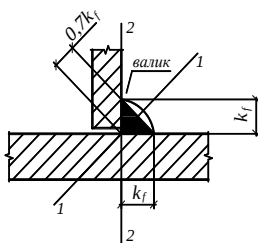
Схема расчетных сечений сварного соединения с угловым швом
